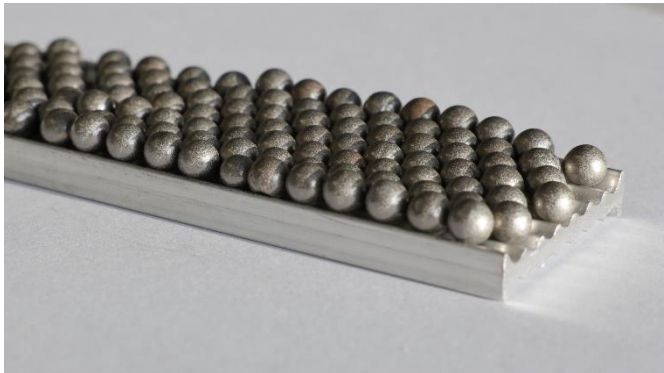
Partikelgefüllte Hohlkugeln auf schäumbarem Aluminium.
